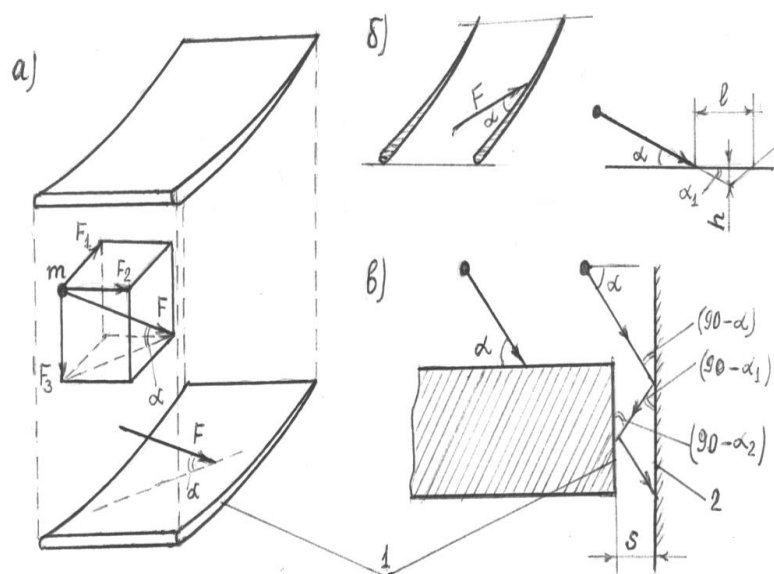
Схема соударения твердой частицы с поверхностью (а и б) и торцевой частью (в) лопасти рабочего колеса осевого насоса : 1-торец лопасти; 2-камера рабочего колеса
